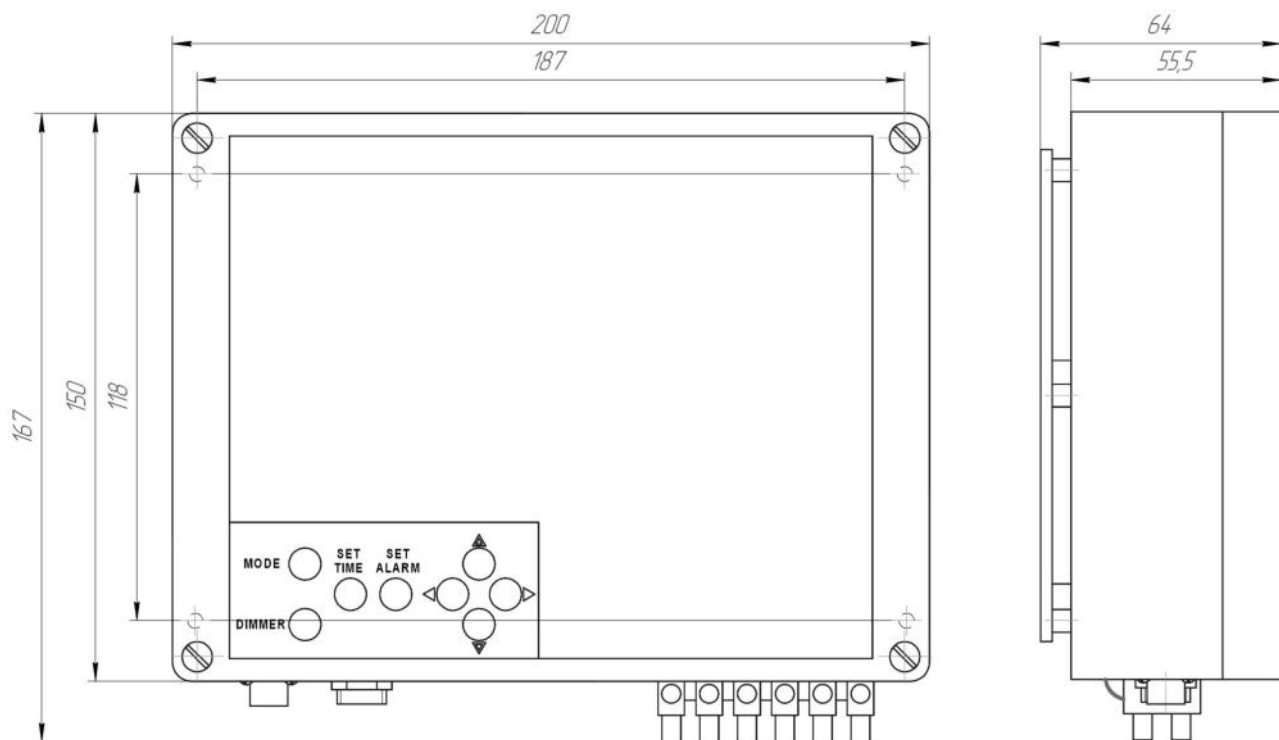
Габаритный чертеж ИПСС-02, ИПСС-03
